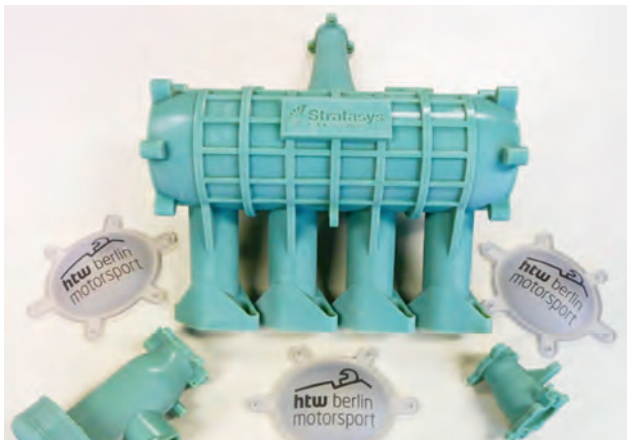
Воздушный короб, напечатанный на 3D-принтере
